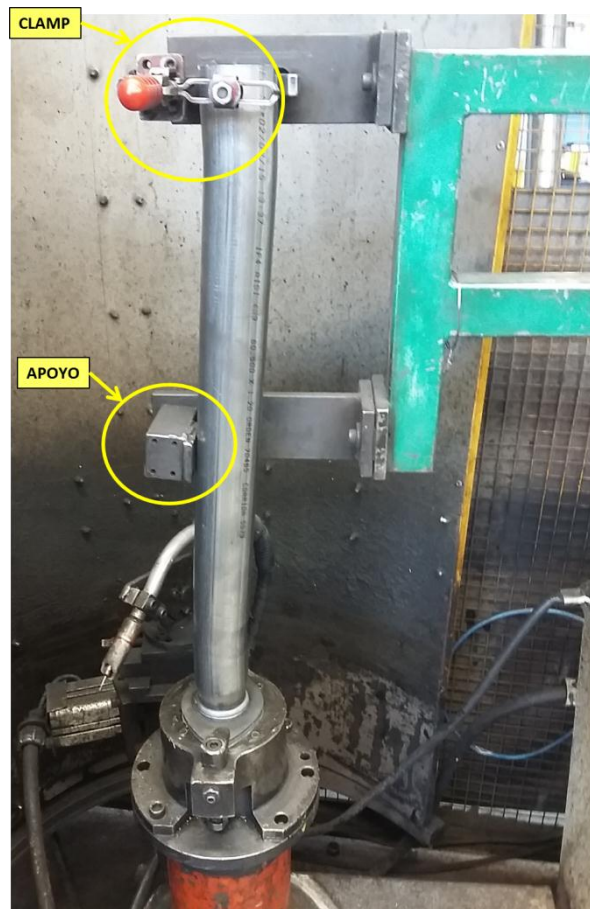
MÉTODO DE SUJECCIÓN DE TUBO EN DISPOSITIVO DE SOLDADURA MÁQUINA TORCHA GIRATORIA
